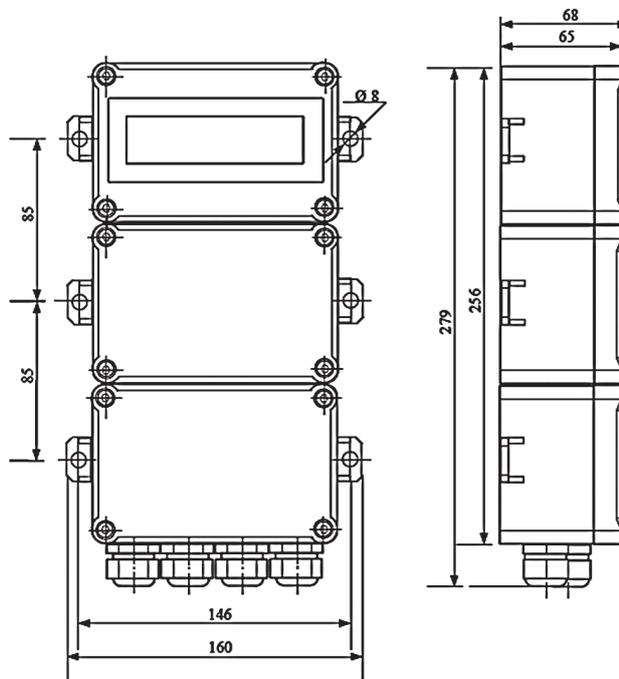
а Габаритные размеры преобразователя MERA 600Ex (корпус ОВ 3-Р154-0000333)
